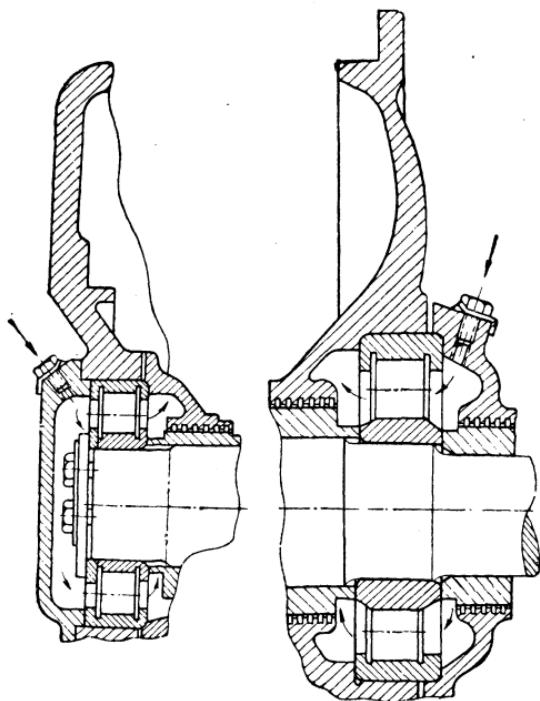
Смазка якорных подшипников мотор-компрессора НБ-431
